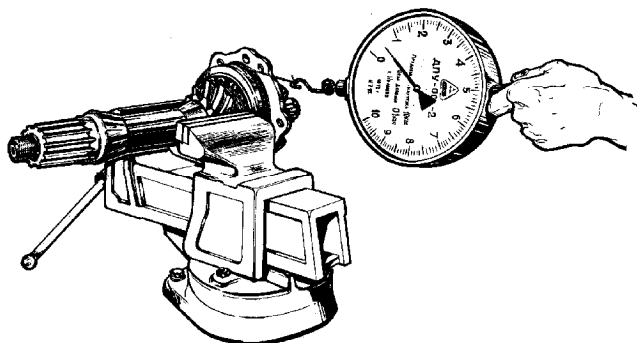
Проверка регулировки подшипников ведущей конической шестерни
